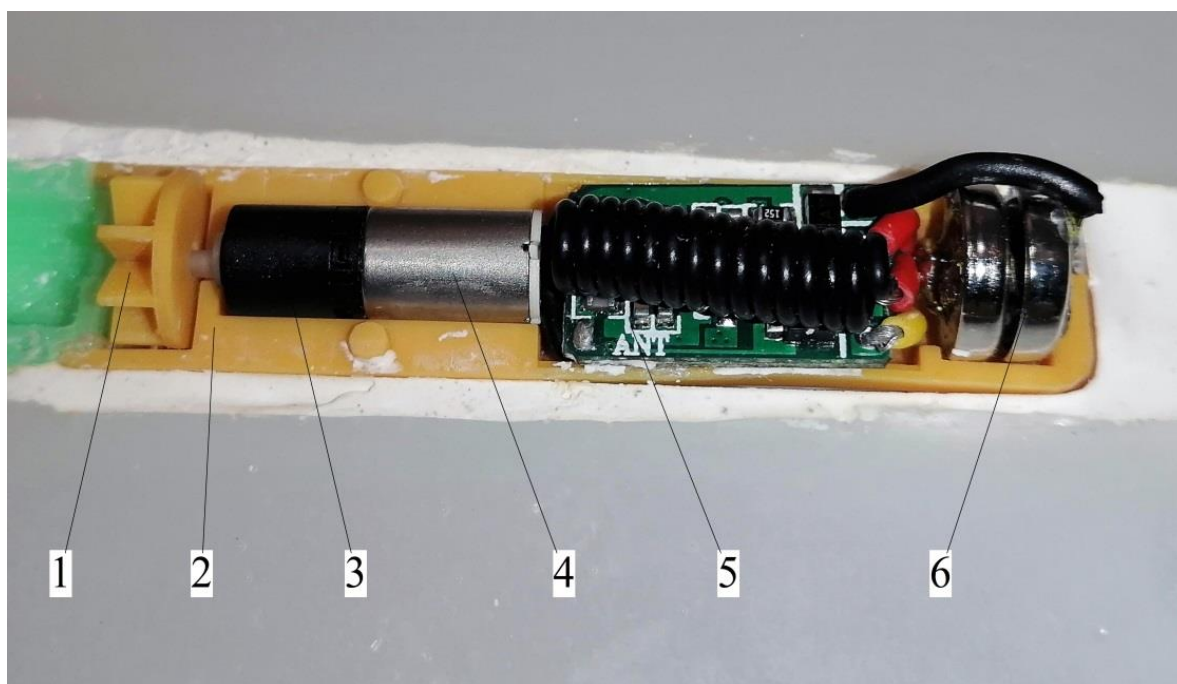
Корпус в разрезе: 1 – крыльчатка микронасоса, 2 – корпус, 3 – редуктор электродвигателя, 4 – электродвигатель, 5 – приемник радиосигнала, 6 – элементы питания
